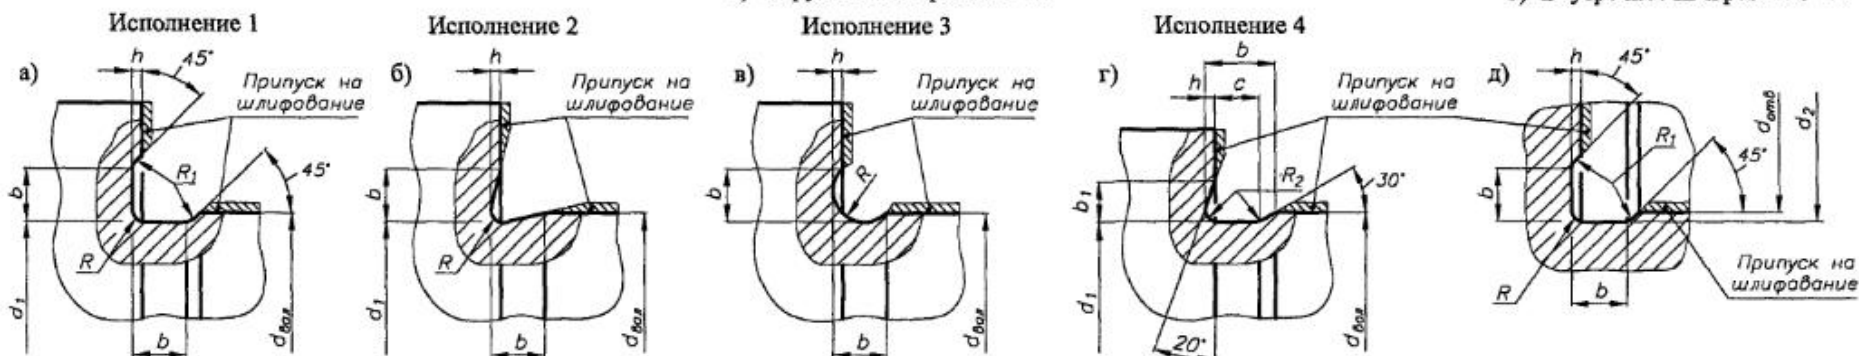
Канавки для выхода шлифовального круга при шлифовании по цилиндру и торцу
